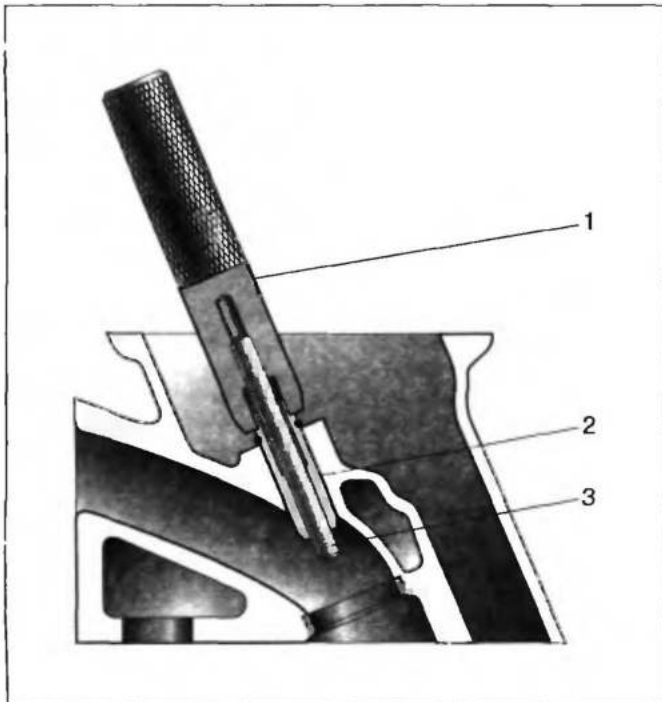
Оправка для запрессовки направляющих втулок клапанов ударным способом:
